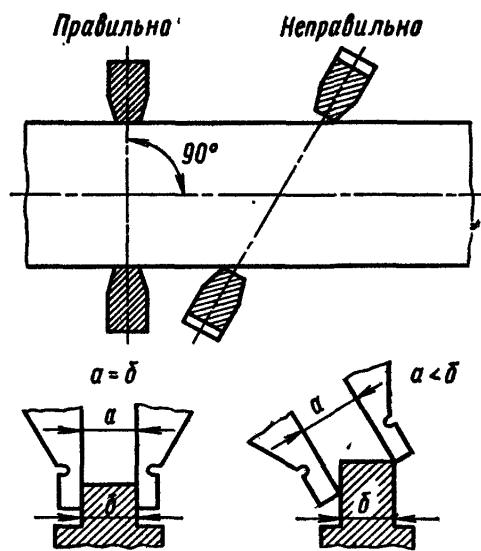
Установка штангенциркуля при измерении наружных поверхностей
